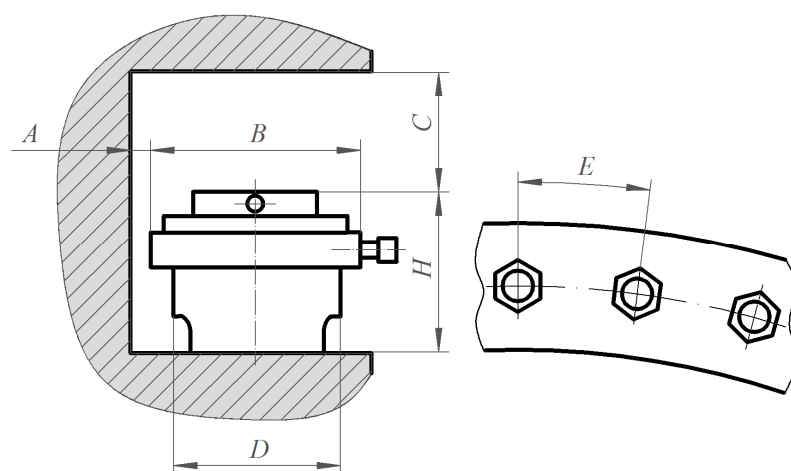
Схема к выбору размеров деталей для установки гидроключа для сборки резьбового соединения
